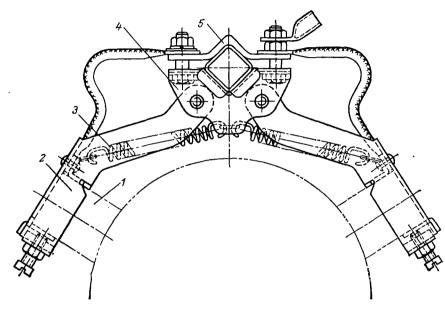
Симметричный парный щеткодержатель асинхронного двигателя с фазным ротором:
